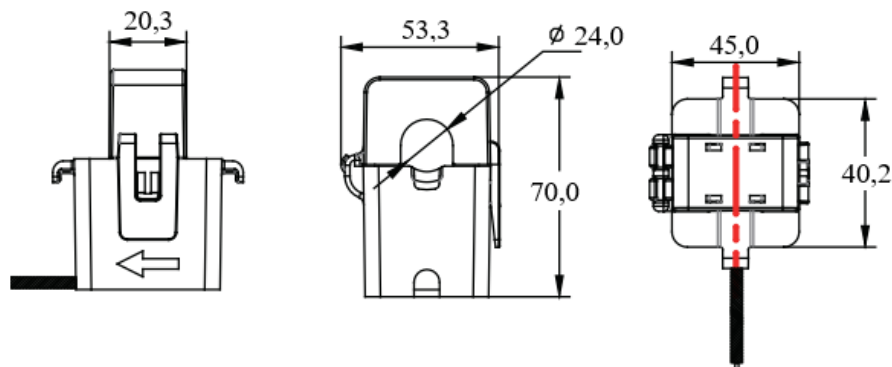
Внешний вид и габаритные размеры датчика SCT200
